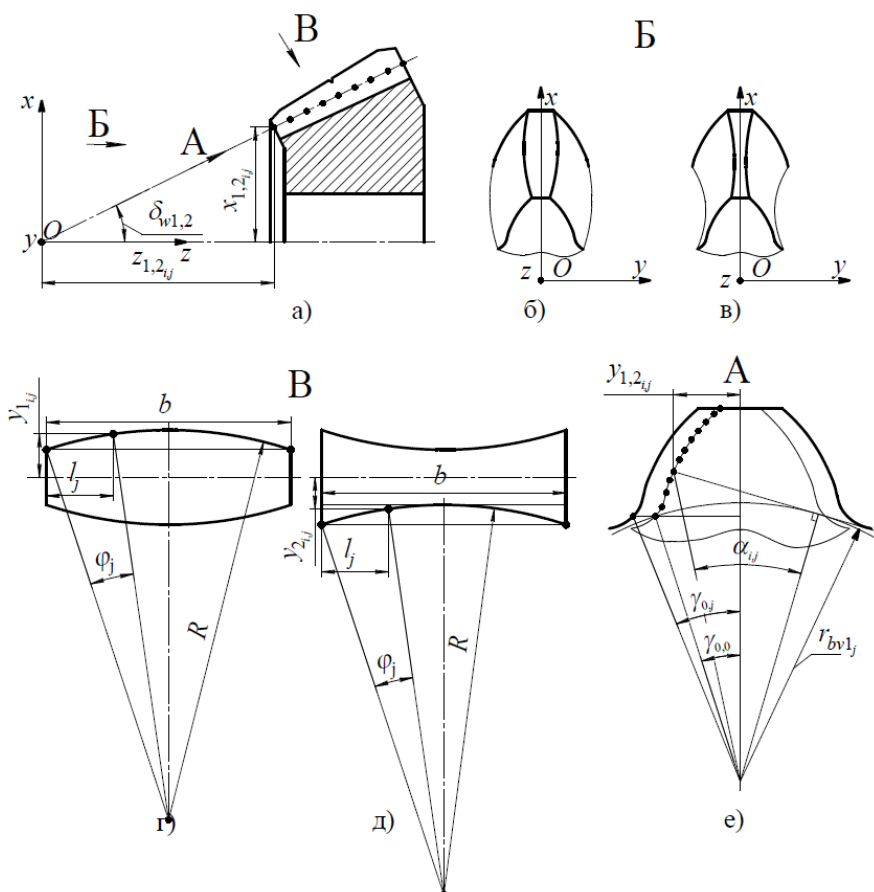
До математичного опису бічної робочої поверхні ДОВ зубців шестірні й колеса конічної передачі: а) шестірня або колесо в системі координат $Oxyz$; б) зуб шестірні; в) зуб колеса; г) до розрахунку координати $y_{1,i,j}$ шестірні; д) до розрахунку координати $y_{2,i,j}$ колеса; е) до розрахунку координат $x_{1,2,i,j}$, $y_{1,2,i,j}$, $z_{1,2,i,j}$
